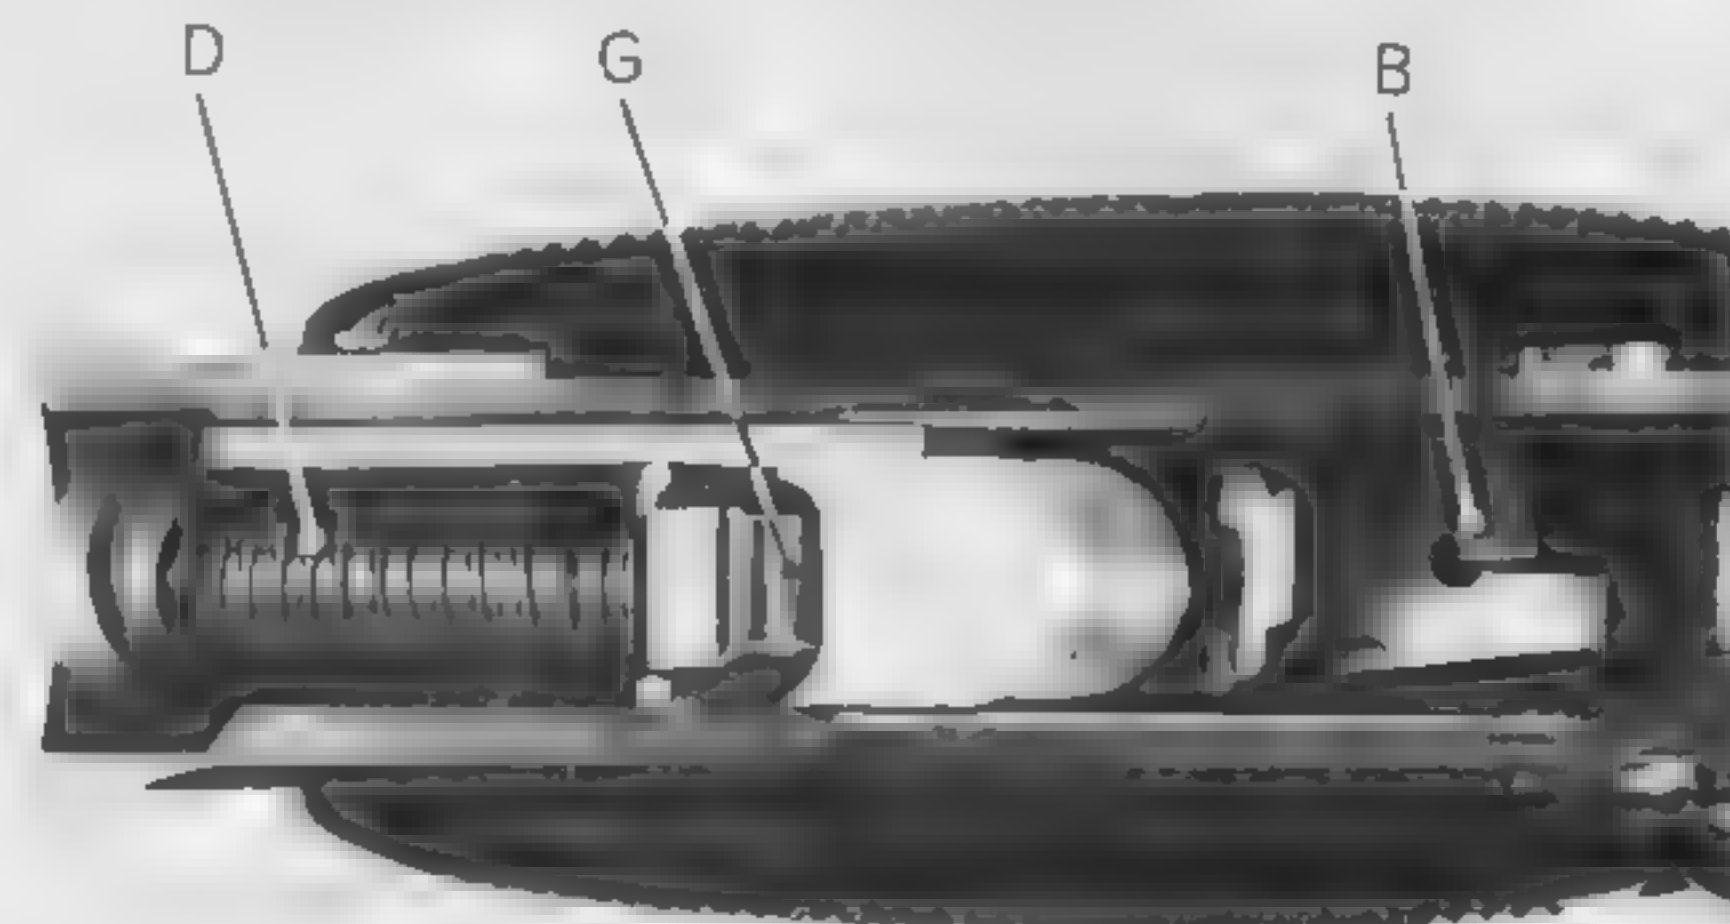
Blick von oben in das Gehäuse. B = Blattfeder, D = Abzugsfeder, G = Abzugstollen.
